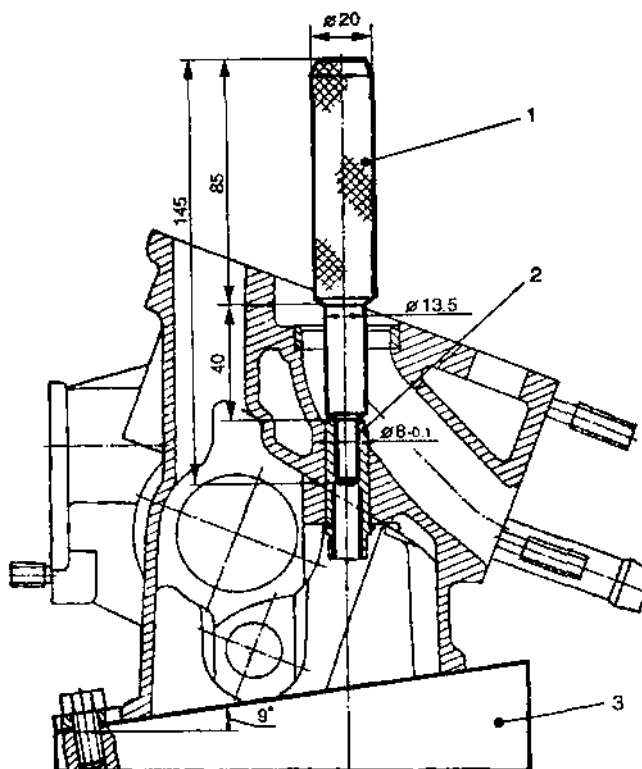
Оправка для выпрессовки направляющей втулки клапана:
